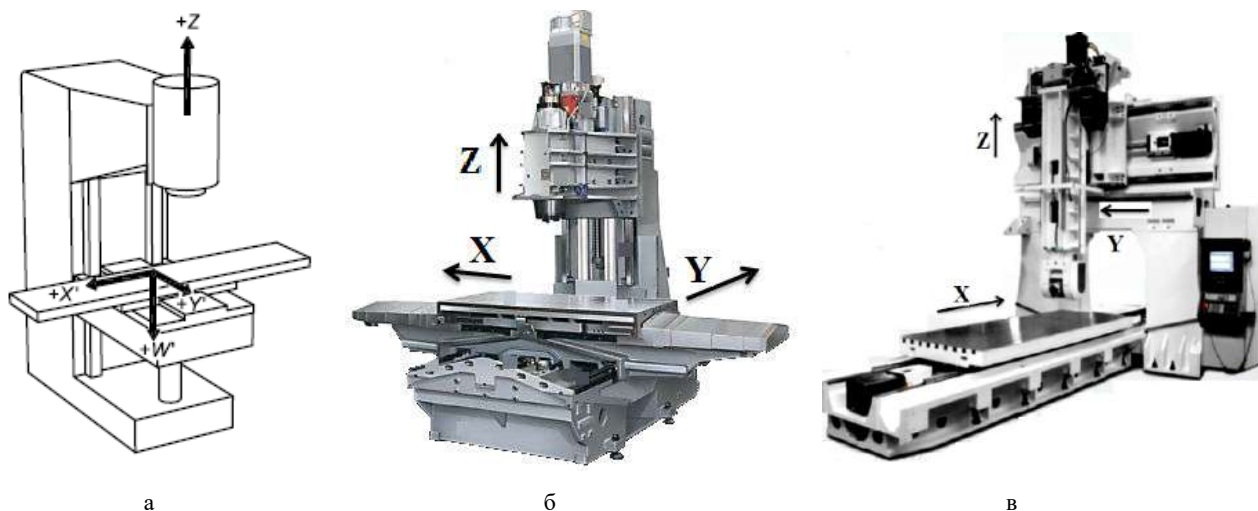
Компонування фрезерних верстатів з ЧПК
